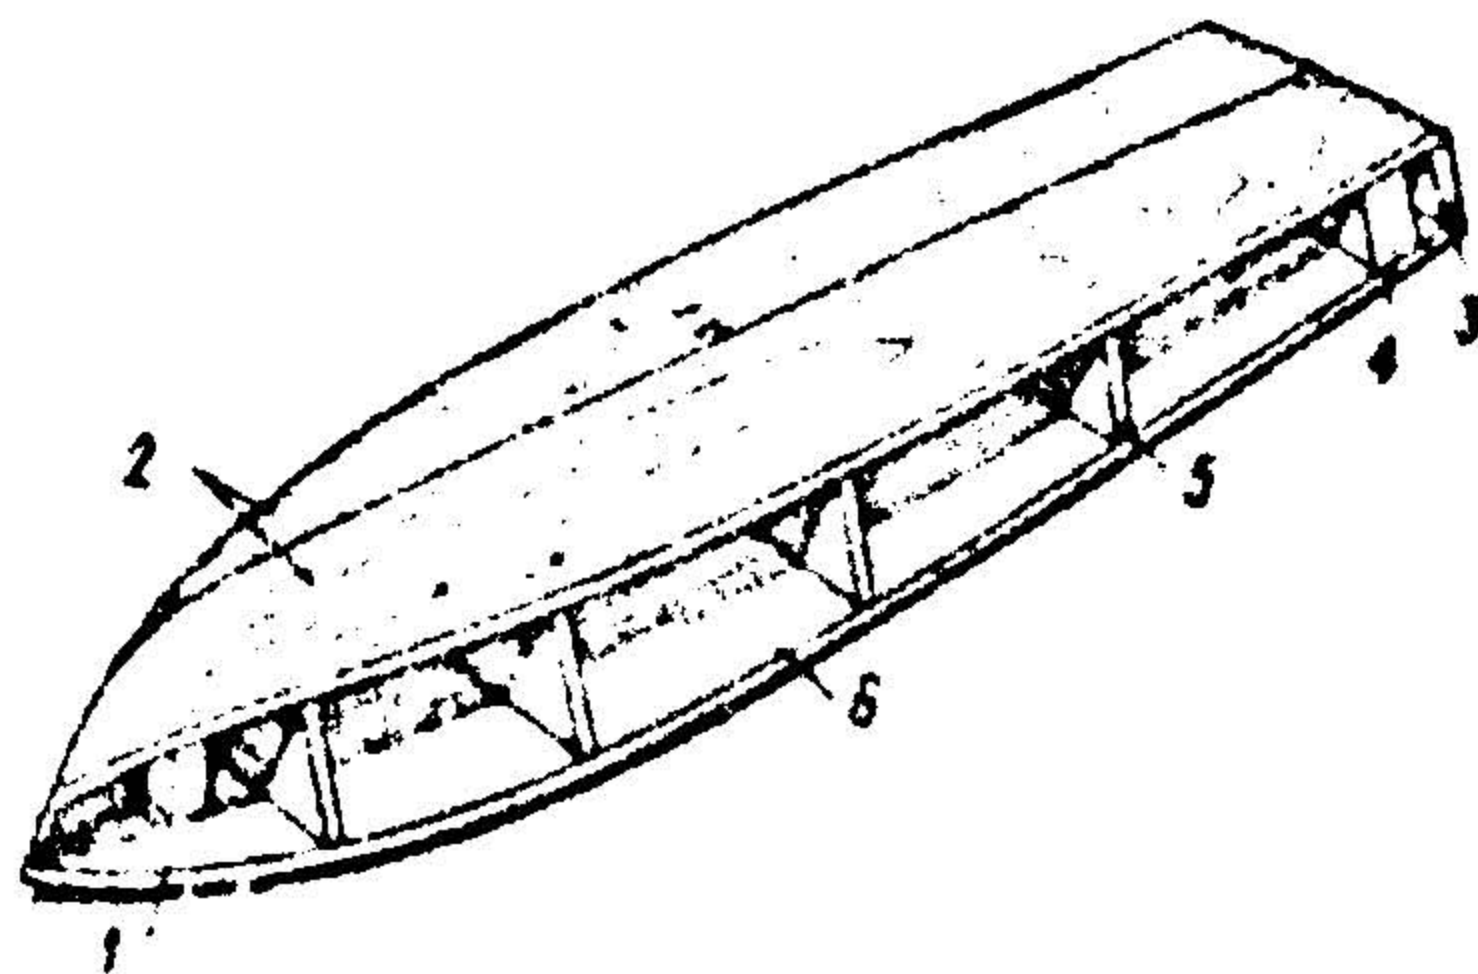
Обшивка корпуса: 1 — носовой брусок; 2 — подводная часть обшивки; 3 — транцевая доска; 4 — кормовой брусок; 5 — шпангоут; 6 — настил палубы
